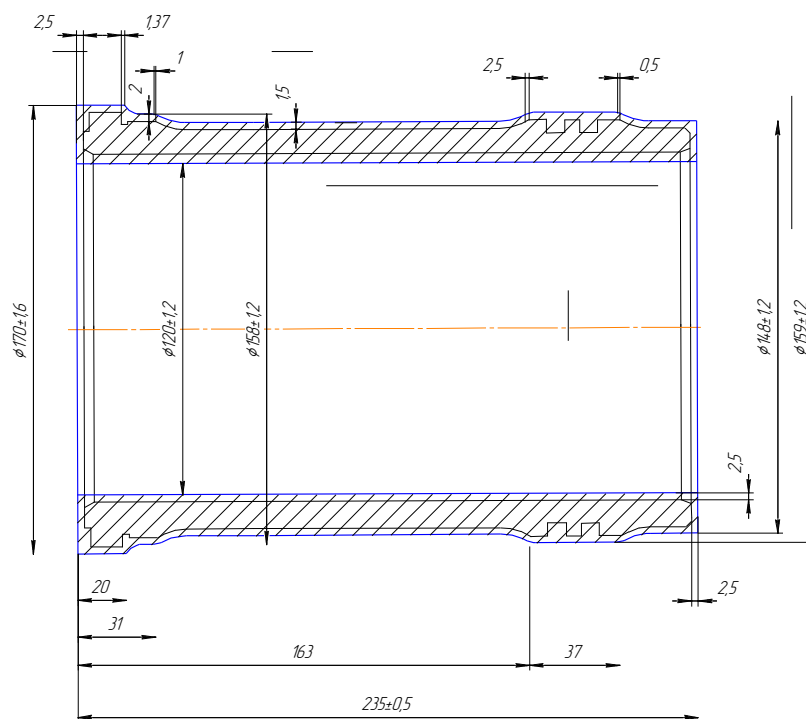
Ескіз заготовки гільзи циліндра
